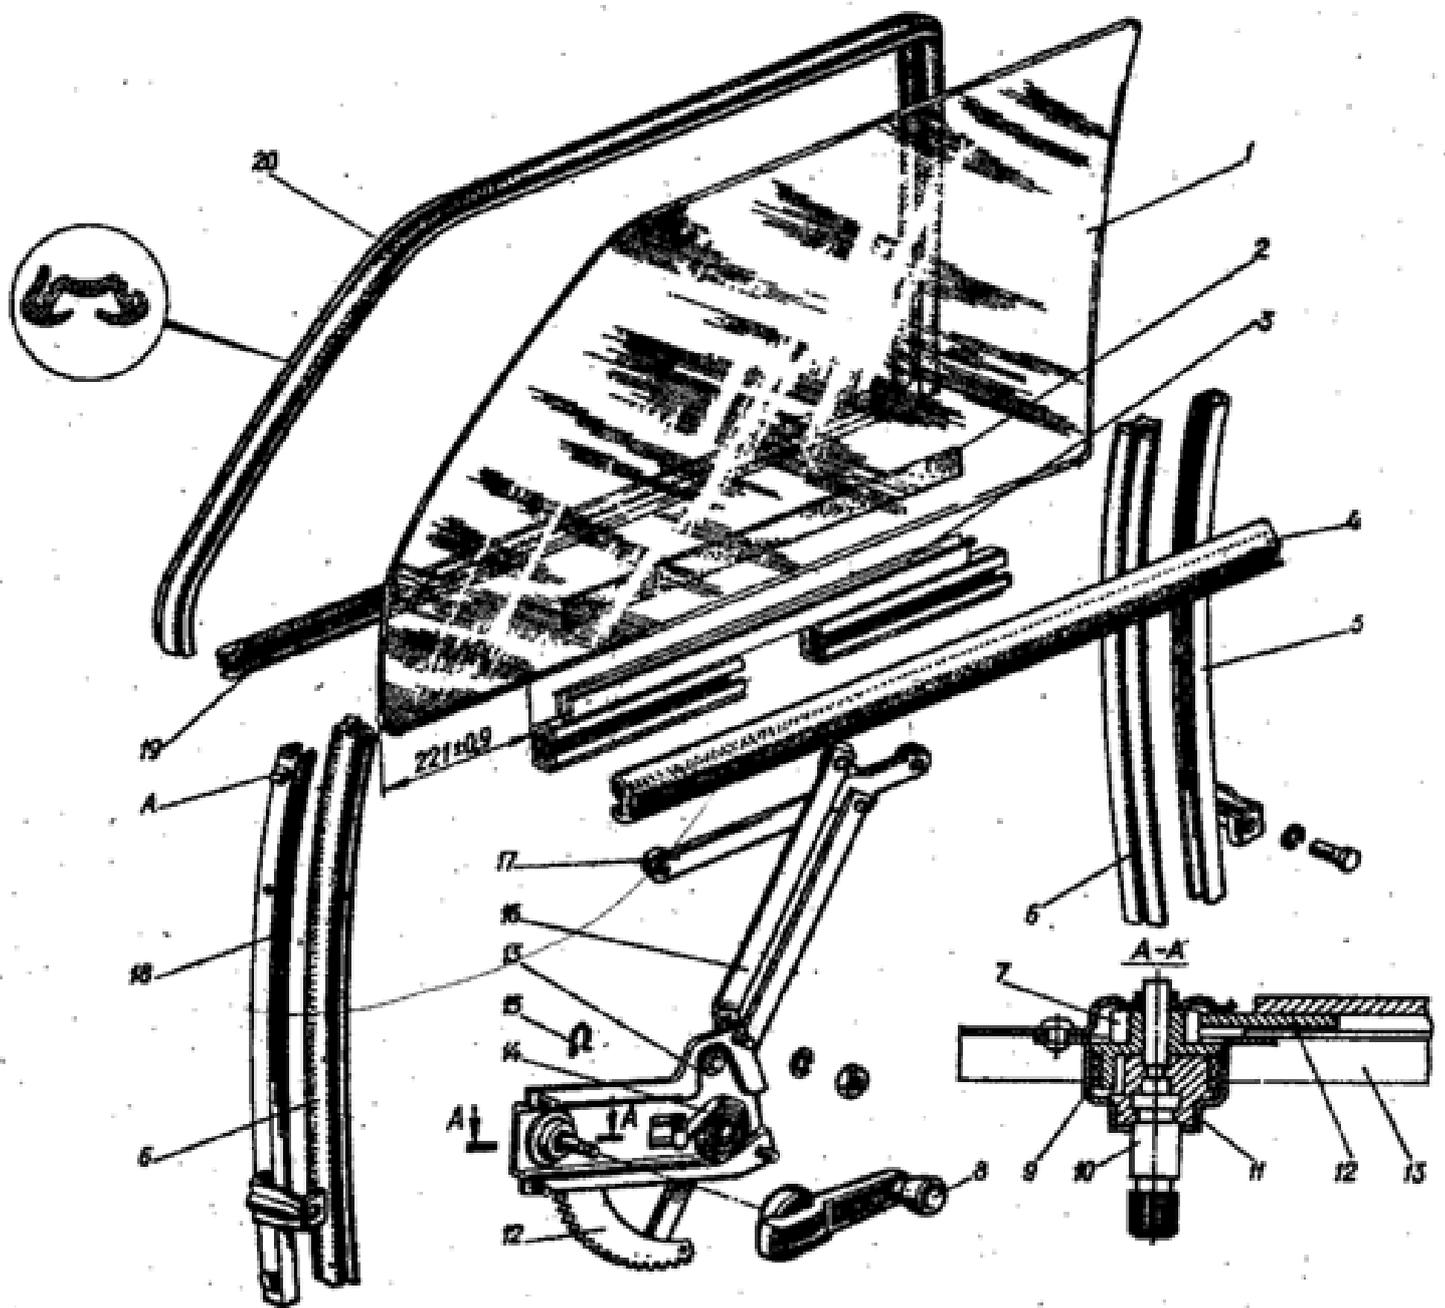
Стеклоподъемник, стекло и уплотнители боковой двери трехдверного автомобиля: 1 - стекло двери; 2 - прокладка стекла; 3 - обойма стекла; 4 - уплотнитель подоконный левый; 5 - стойка стекла правая; 6 - уплотнитель; 7 - шестерня ведомая; 8 - ручка; 9 - пружина торсионная; 10 - вал тормозного механизма в сборе; 11 - корпус; 12 - зубчатый сектор с нижним рычагом; 13 - кронштейн; 14 - пружина противовеса; 15 - пружина стопорная; 16 - рычаг верхний; 17 - кулиса роликов; 18 - стойка стекла левая; 19 - уплотнитель подоконный правый; 20 - уплотнитель стекла верхний; Б - подштампованный язычок.
